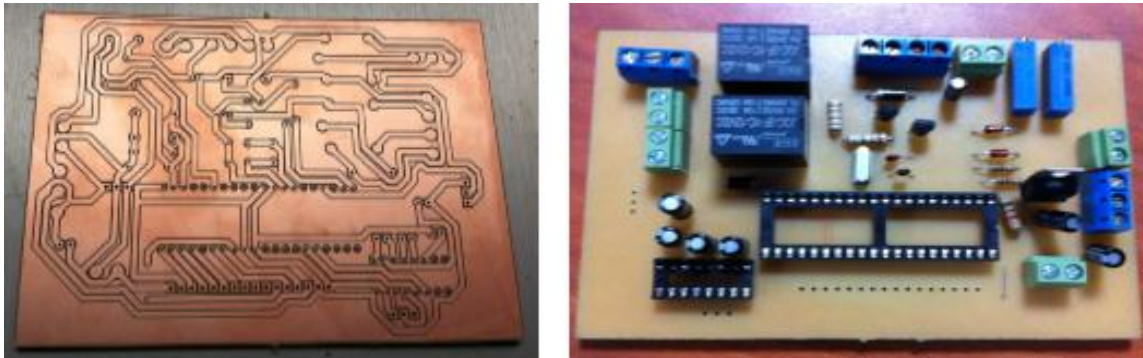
PCB CIRCUITO DE CONTROL FISICO
